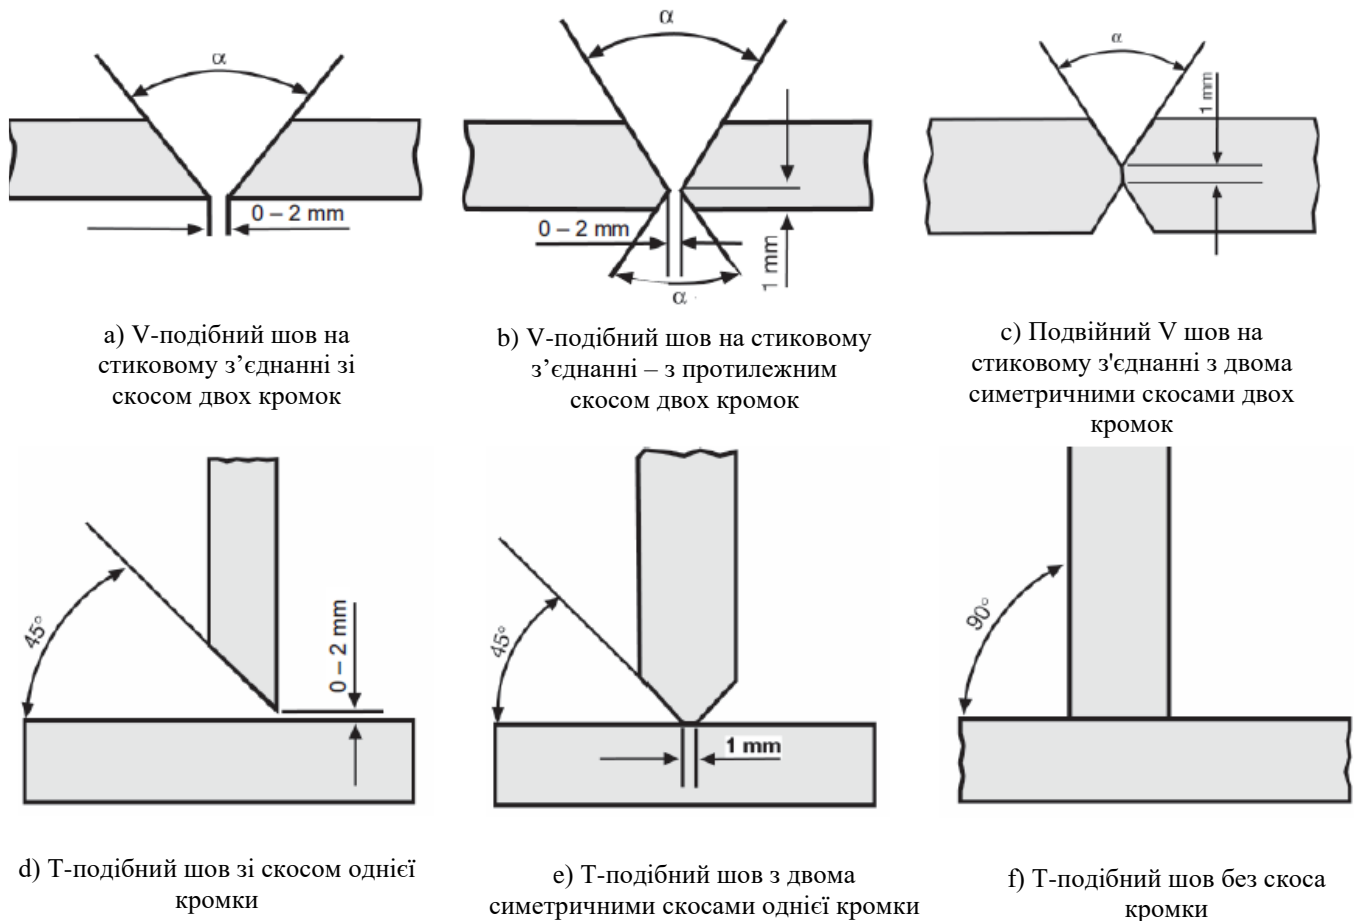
Форми обробки кромки для зварних швів
